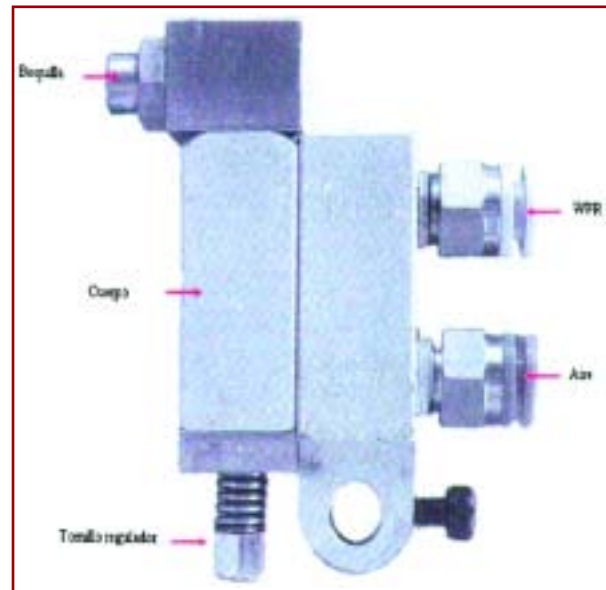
Boquilla WFS-05G-R, de Yamaguchi Giken.
